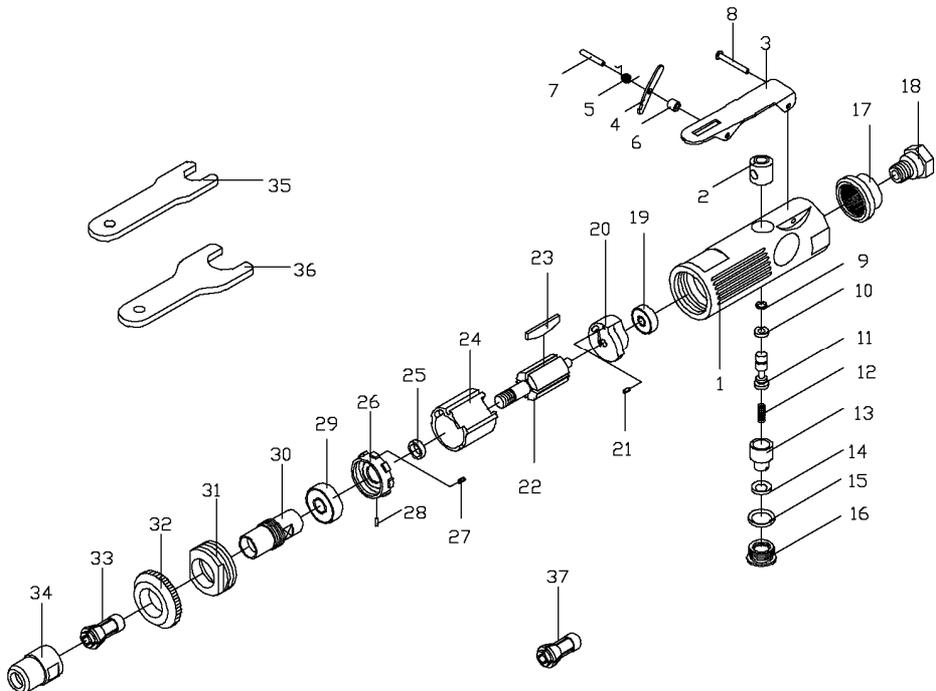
Схема устройства и сборки бормашины ручной пневматической MFG-125/001-1
